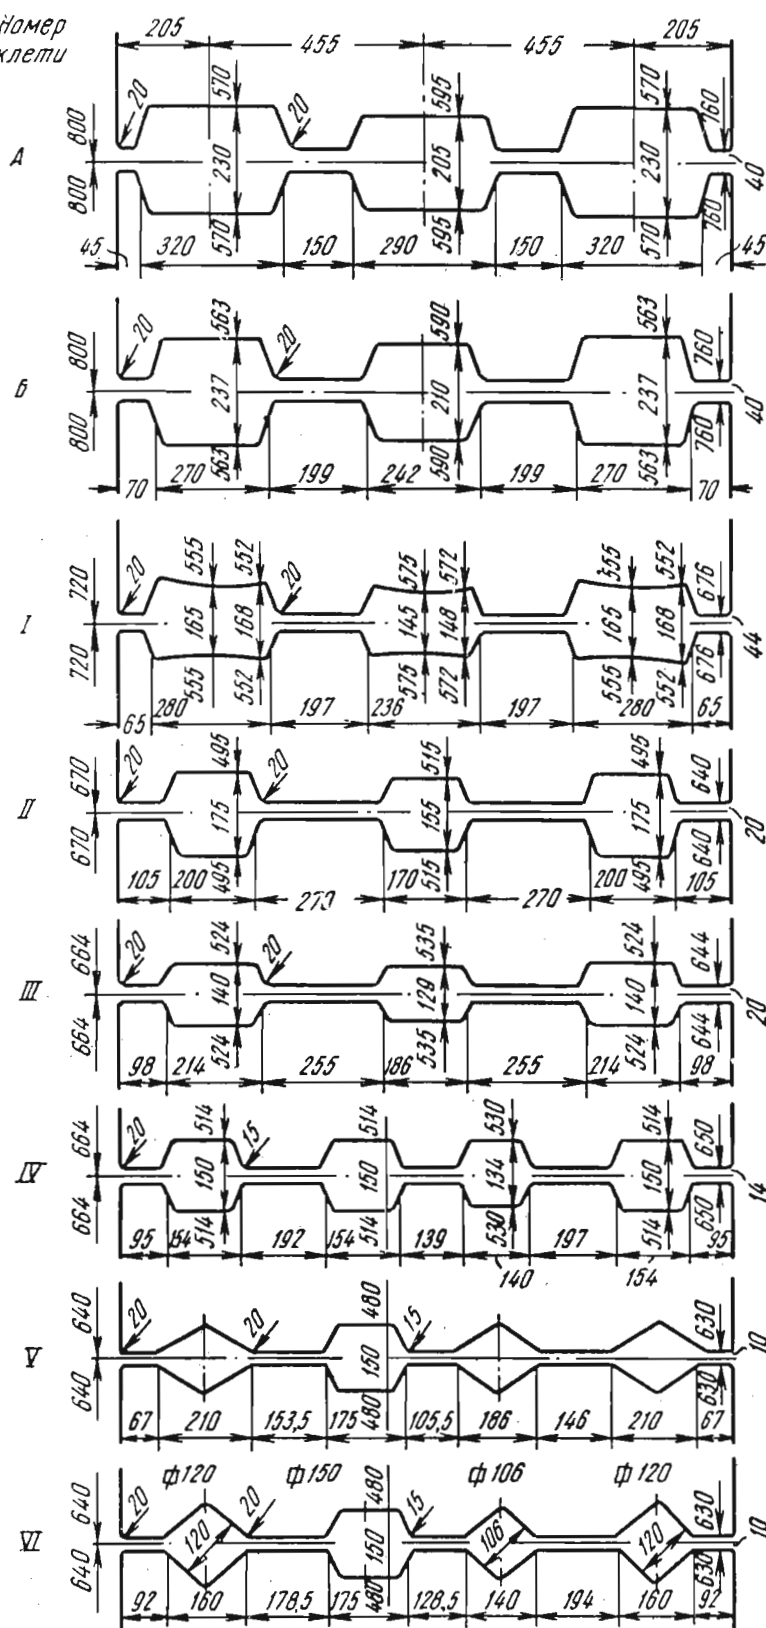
Калибровка валков непрерывного заготовочного стана 630 для прокатки заготовок сечением 106×106, 150×150 и 120×120 мм
